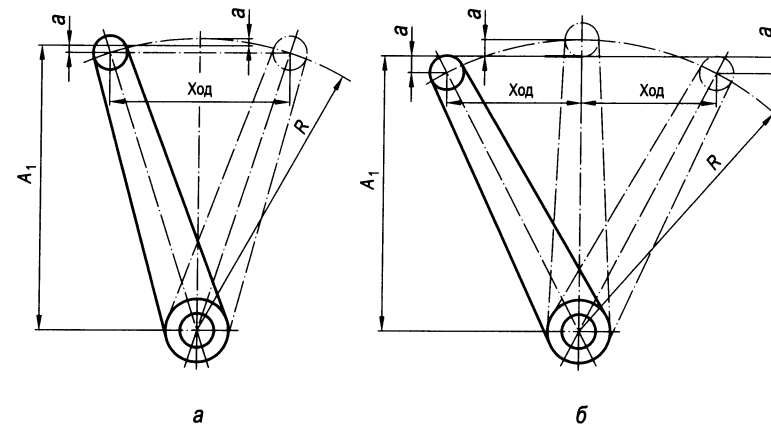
Определение радиуса рычага для двух (а) и трех (б) частот вращения вала ($2a$ – перемещение камня или вилки в пазе блока зубчатых колес; $R = A_1 + a$; ход – осевое перемещение блока зубчатых колес)
